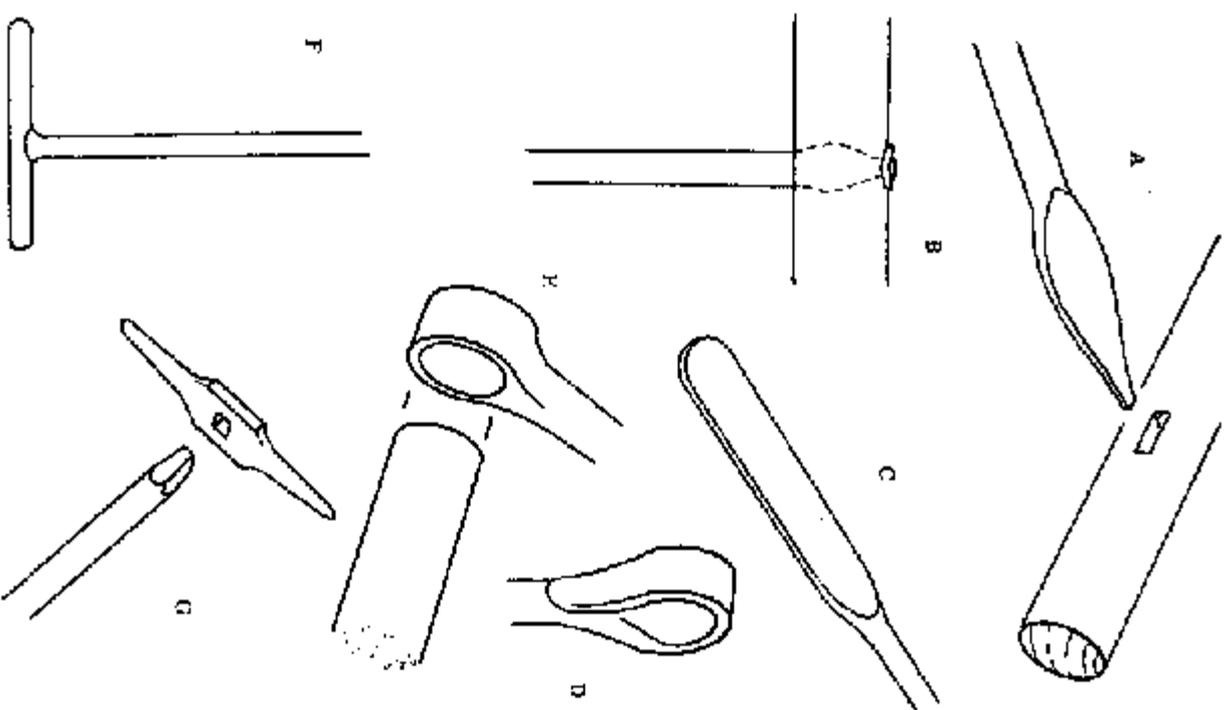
Si la herramienta sirve para dar vuelta a la caña, la unión del mango debe resistir la torsión: (A) una punta plana y alargada; (B) remache con percha redonda; (C) el ojo; (D) soldar; (E) forjar el ojo; (F) se solda un maneral en T; (G) se reducen y sujetan los extremos de la barra.
